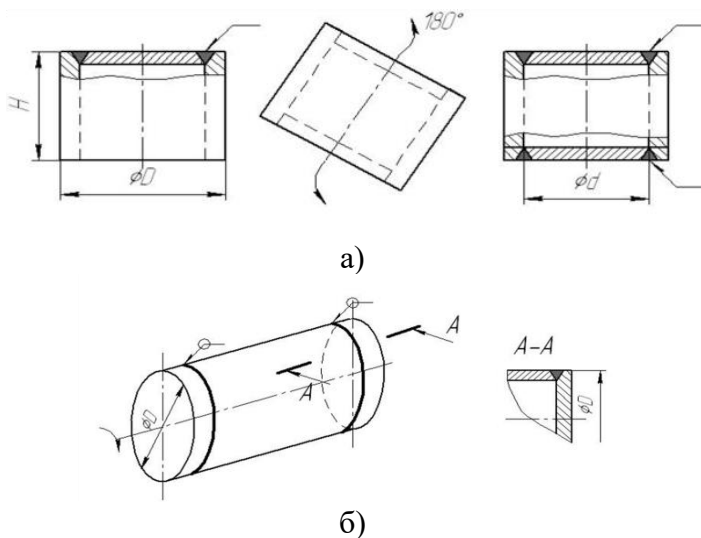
Варіанти зварювання днищ циліндра:
